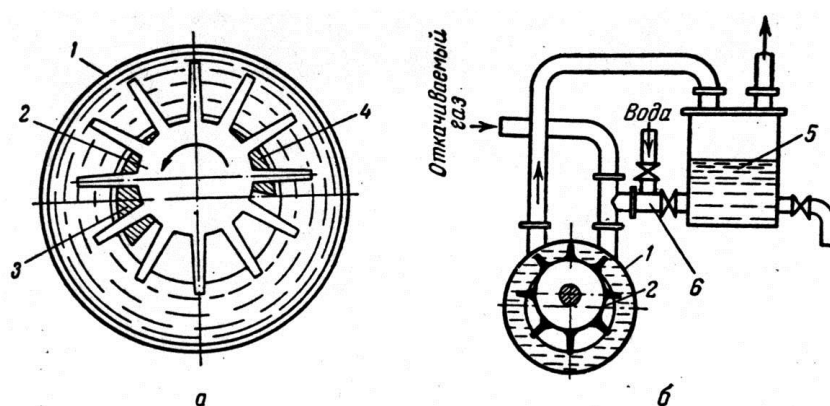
Схема ротационного водокольцевого компрессора (а) и схема его установки для откачки газов (б):
